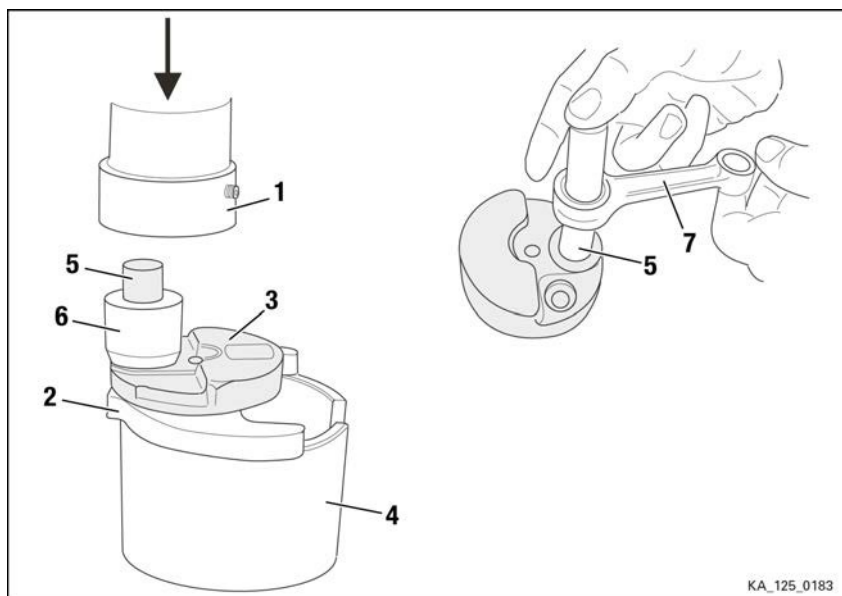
Crankshaft assembly 組裝曲軸
